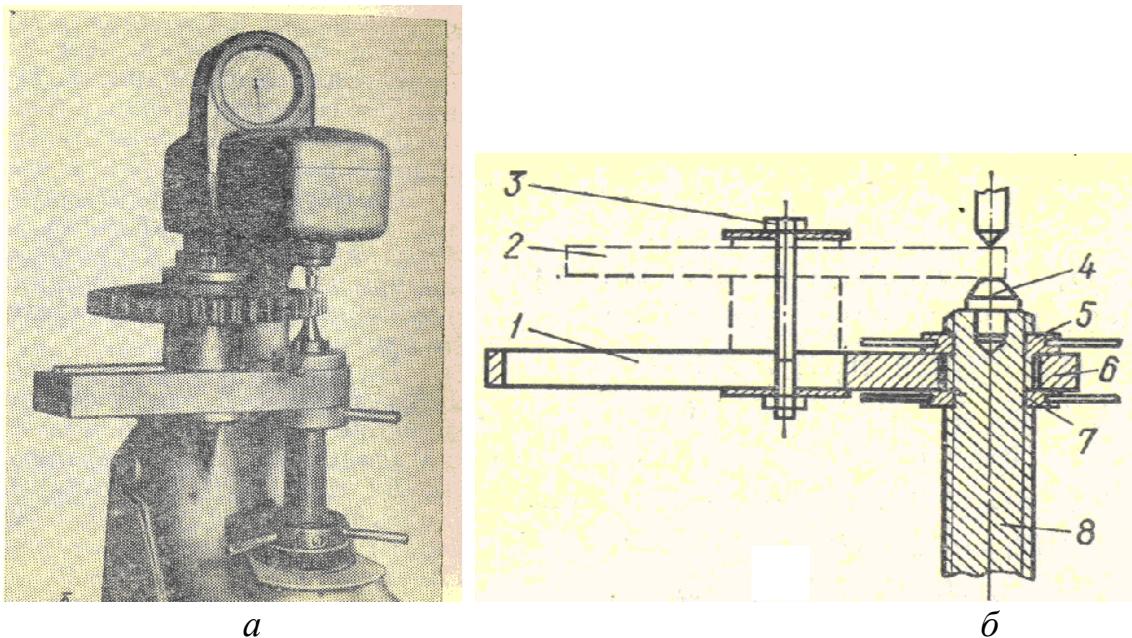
Приспособа для вимірювань зубьев шестерень: а – розположення приспособи на твердомірі Роквела; б – приспособа: 1 – продовжний паз, 2 – шестерня; 3 – болт кріплення; 4 – столік; 5 и 7 – прижімна і опірна гайки; 6 – кронштейн; 8 – гвінт приспособи.
